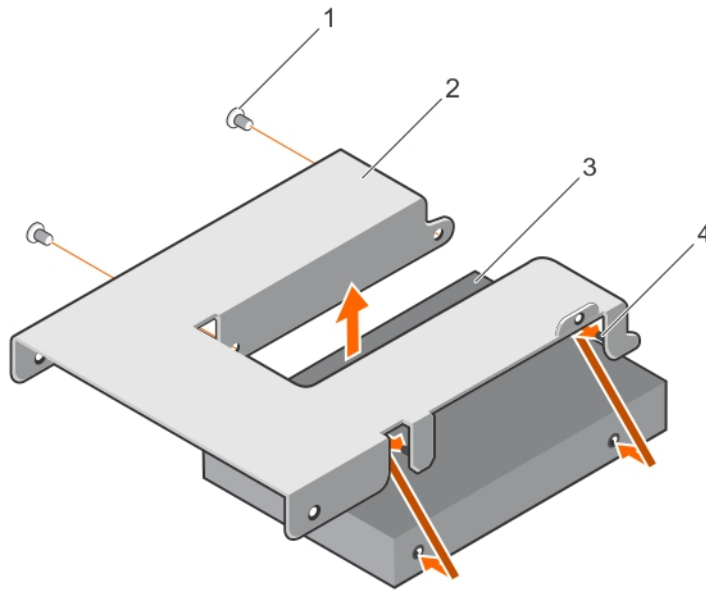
Entfernen und Installieren einer 2,5-Zoll-Festplatte aus einem bzw. in einen 3,5-Zoll-Festplattenadapter
